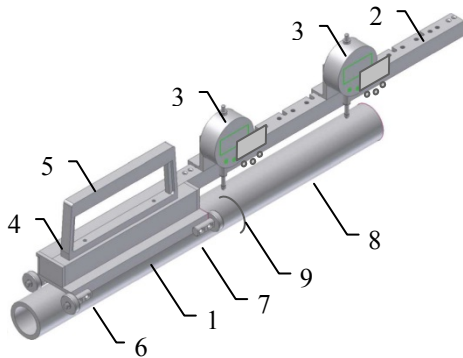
Конструкция измерительного блока: 1 – основание; 2 – штанга; 3 – индикаторы; 4 – корпус; 5 – ручка; 6 – подшипники; 7 – тело трубы; 8 – приваренный замок; 9 – сварной шов
